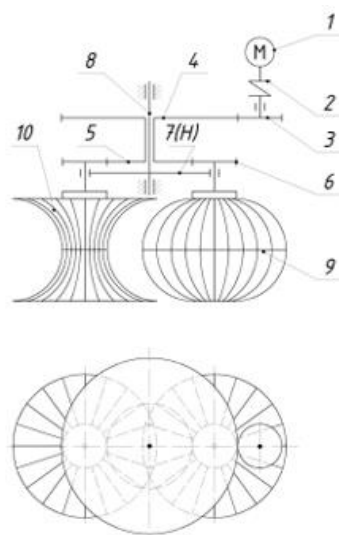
Кинематическая схема двухсателлитного планетарного механизма для привода рабочего органа миксера, где: 1 – электродвигатель, 2 – муфта, 3 – шестерня, 4 – простое зубчатое колесо, 5 – солнечное колесо, 6 – сателлит, 7(H) – водило, 8 – вал, 9 – месильный орган венчика сжатого эллипсоидального вращения; 10 – месильный орган венчика однополюсного гиперболоида вращения.
